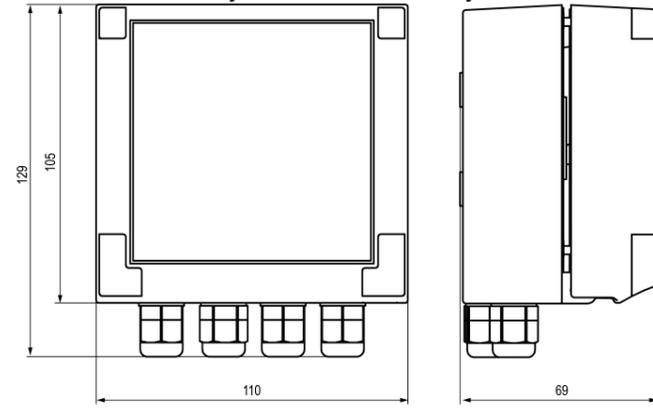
Габаритные размеры прибора в корпусе Н
